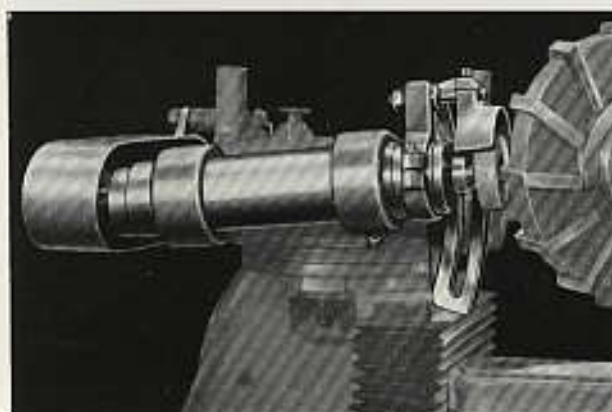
, Anwendung der schrägstellbaren Hilfsschleifspindel beim Radienschleifen an einem Messerkopf
